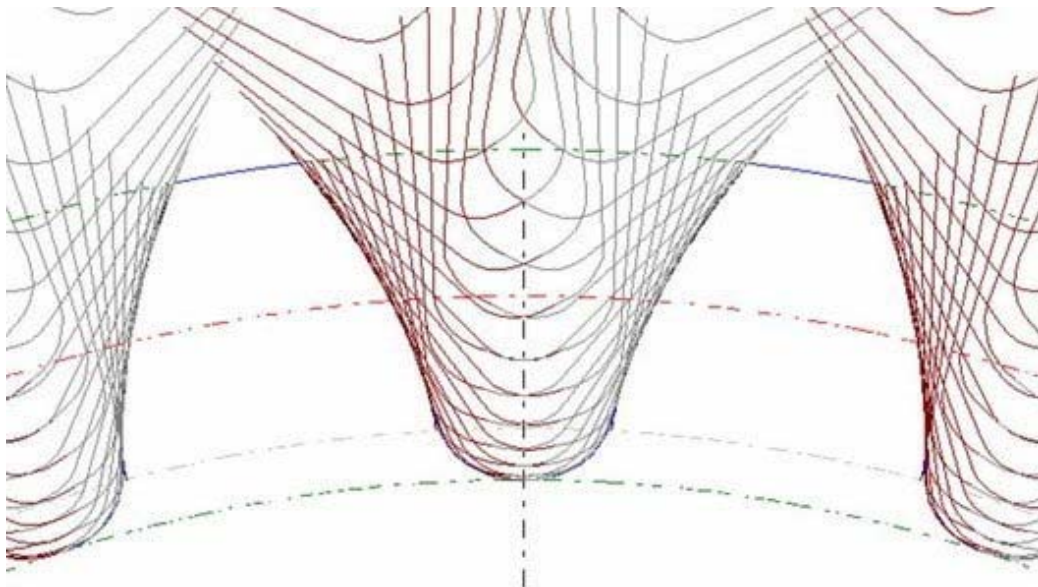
Топография поверхности обработки зубчатого колеса зуборезной рейкой
